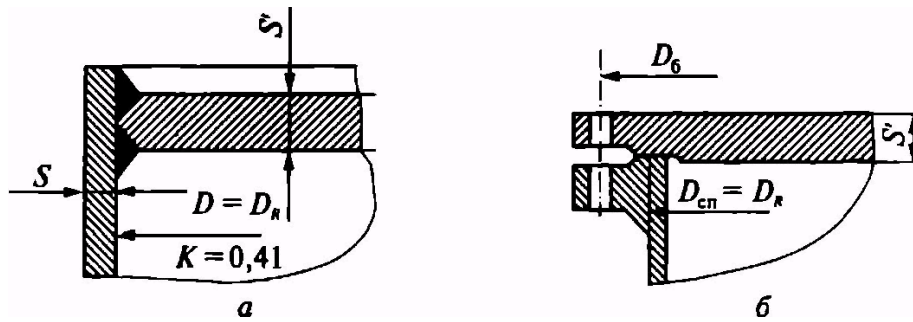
Типы крепления крышки к корпусу аппарата:
